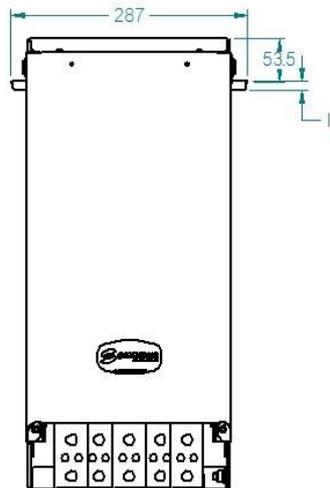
Dimensioni e punti di fissaggio dell'AC/DC UNIT 1050
